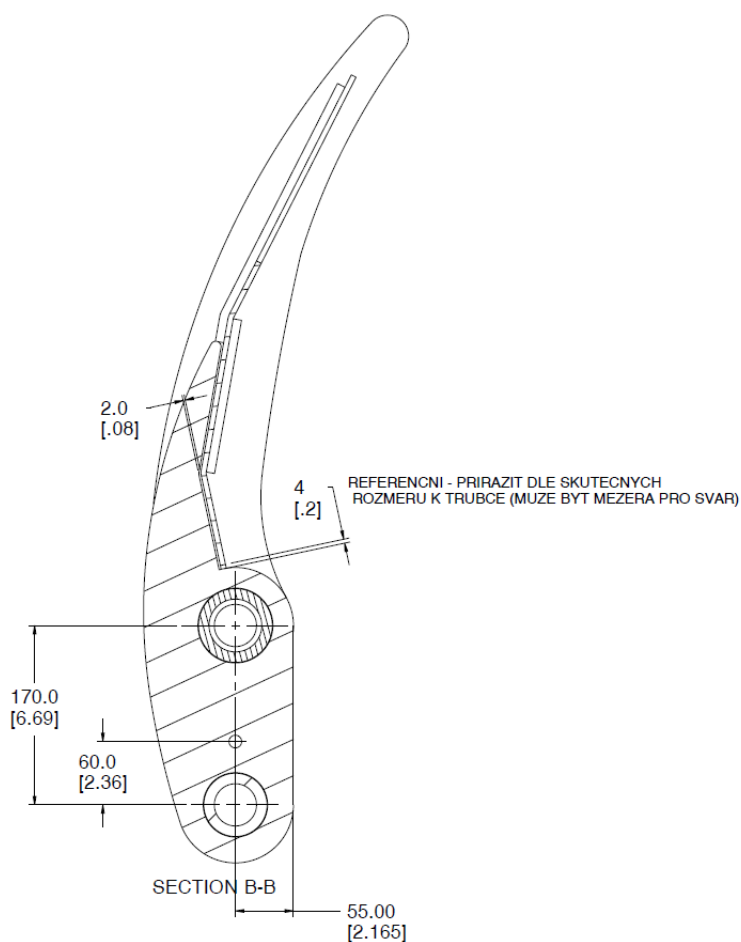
Příklad nevhodně zvolených rozměrových základen
